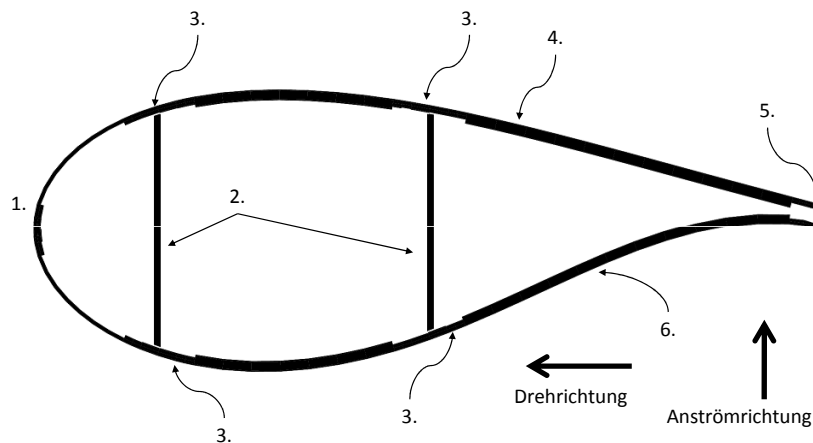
Querschnitt des Rotorblattes M5000- 116
